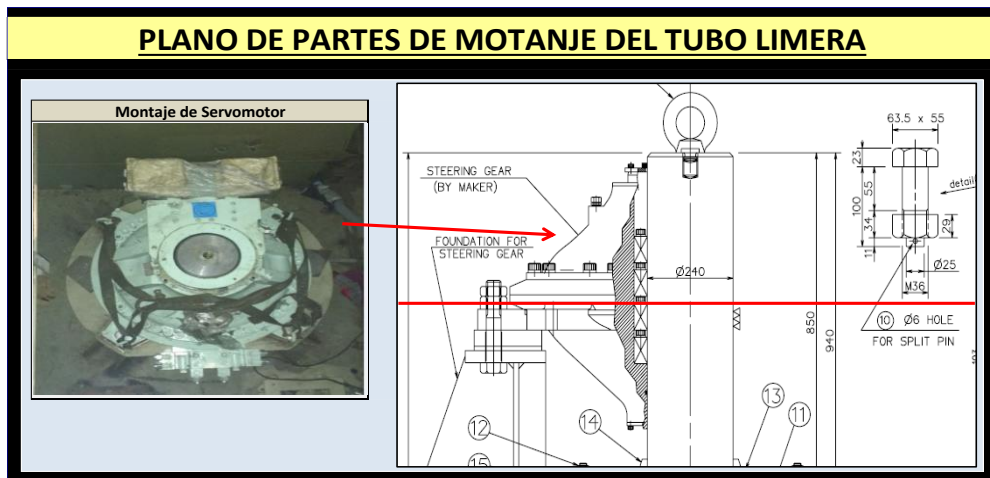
Plano de Partes de Montaje del Tubo Limera
